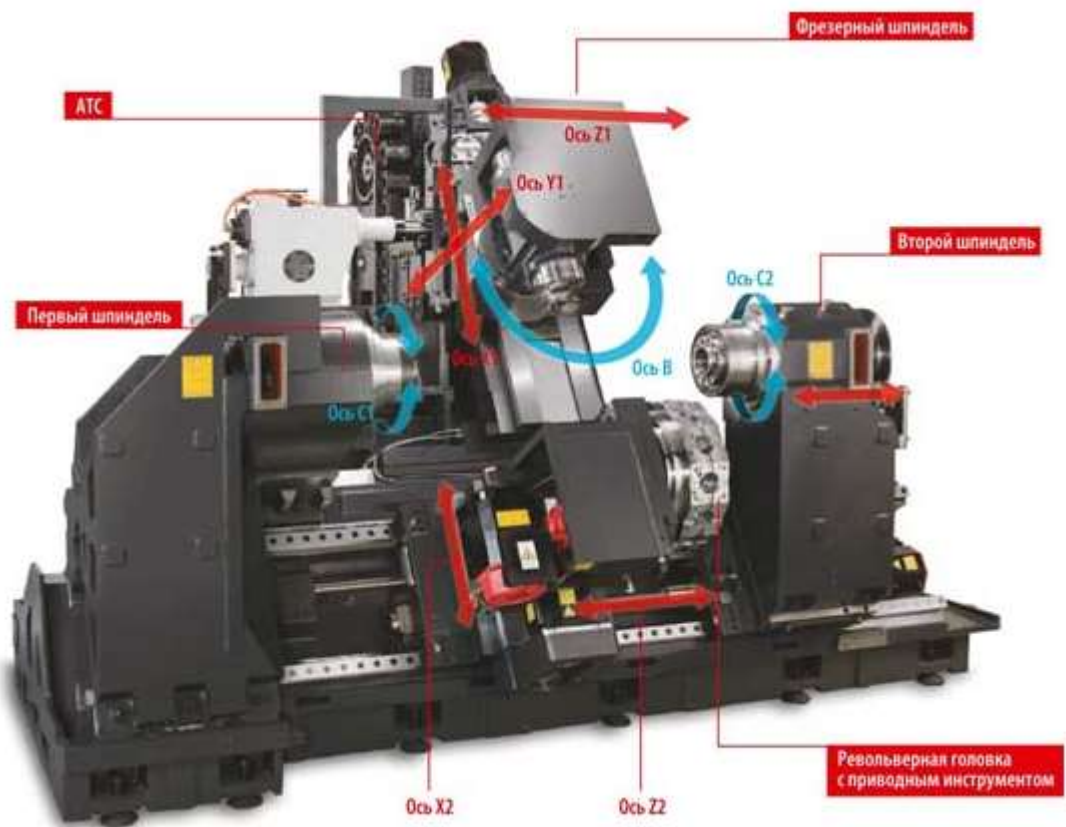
Компоновка токарно-фрезерного центра с ЧПУ Goodway GMS-2000
